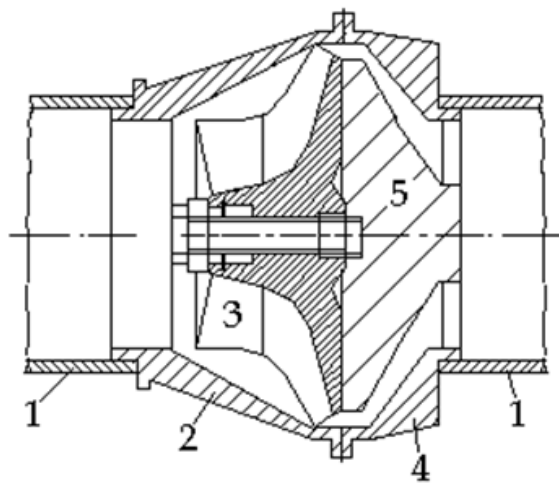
Зоны течения в нескольких каналах, образованных внешней поверхностью детали и внутренней поверхностью приспособления: 1 – рабочие цилиндры установки; 2 – верхняя часть приспособления (переходник); 3 – деталь; 4 – нижняя часть приспособления (направляющая); 5 – основа приспособления [10]
